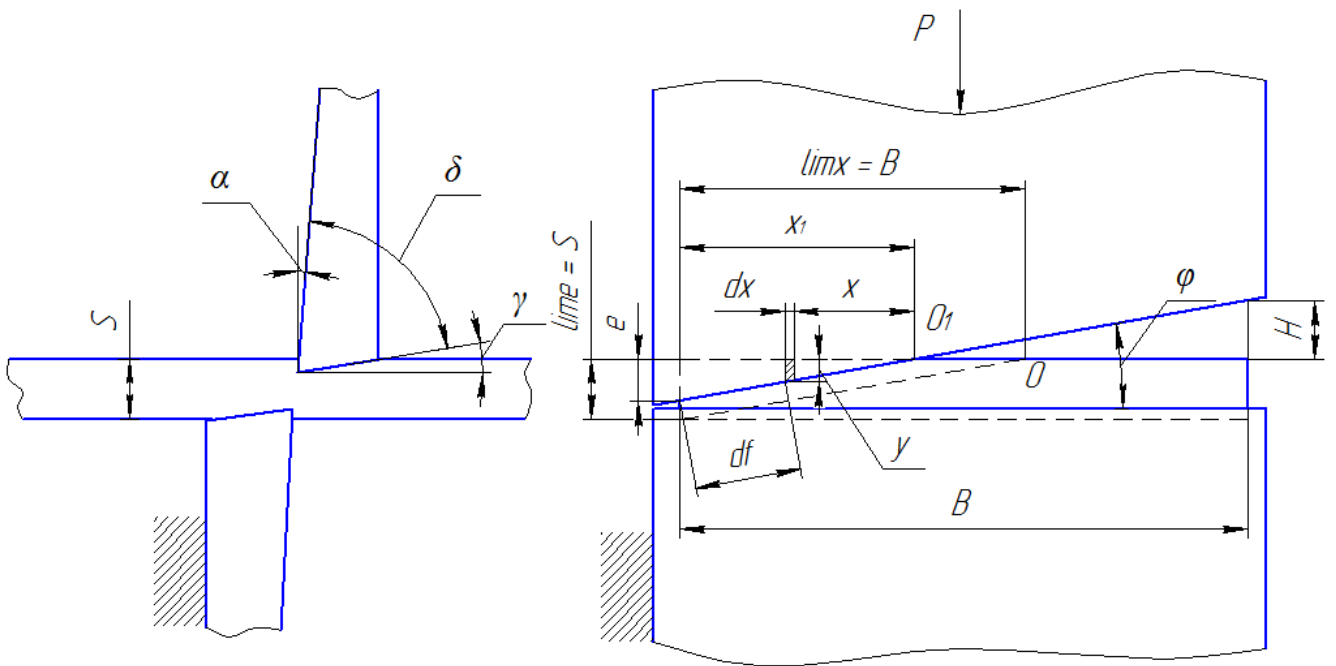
Схема різки ножицями з похилими ножами
